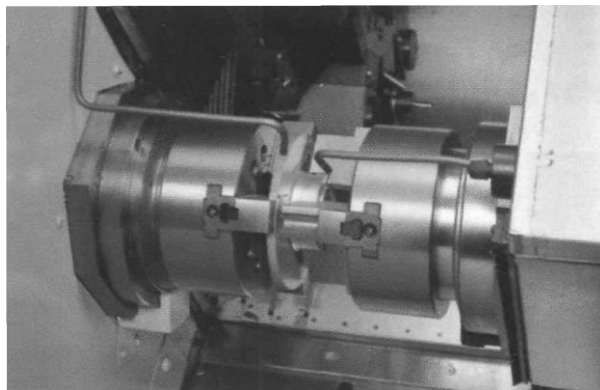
Схема передачі заготовки з кулачка 1 на кулачок 2
